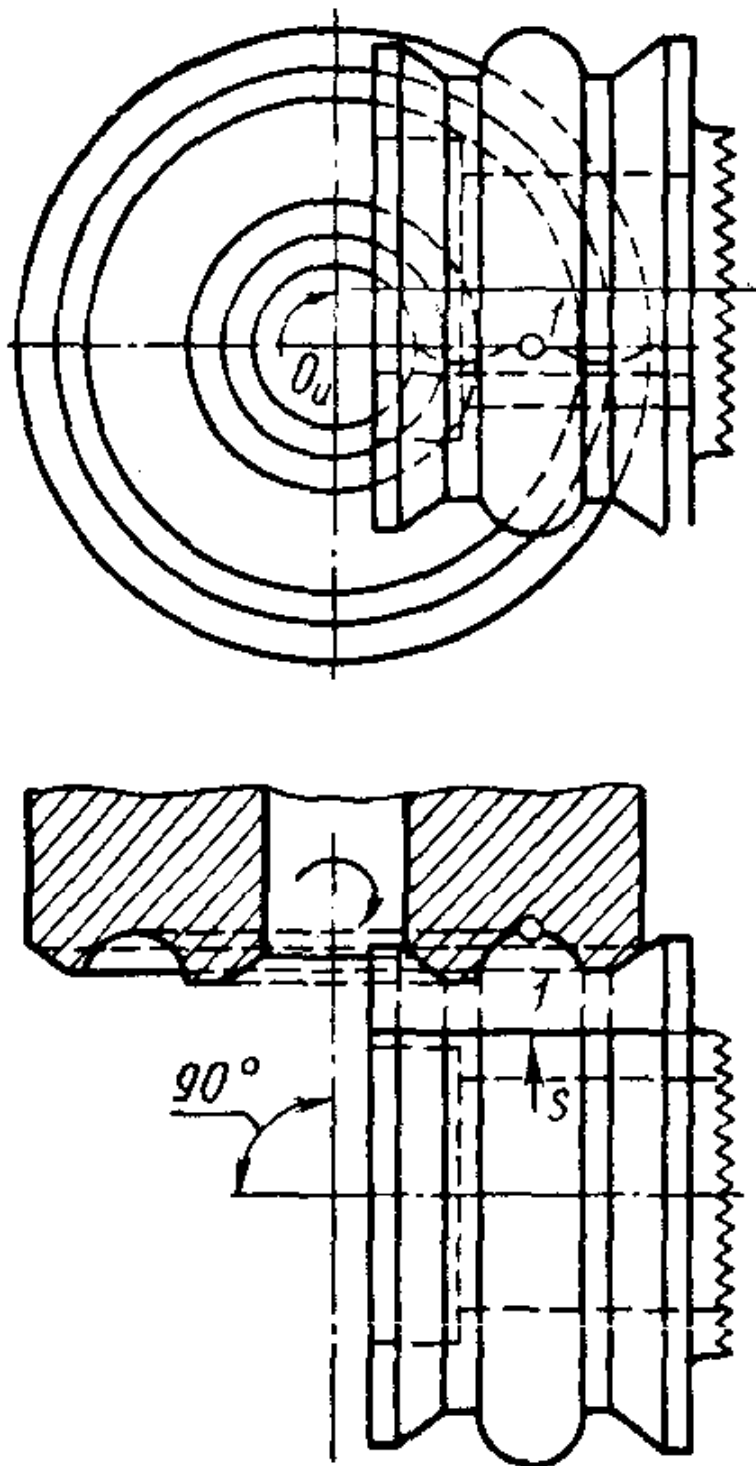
Торцьовий фасонний різець з базою кріплення,
